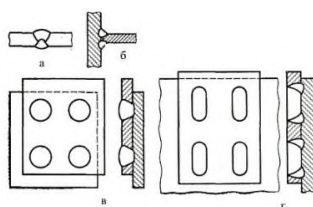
Основные типы сварных швов: а - стыковые; б - угловые; в - пробочные; г – прорезные
